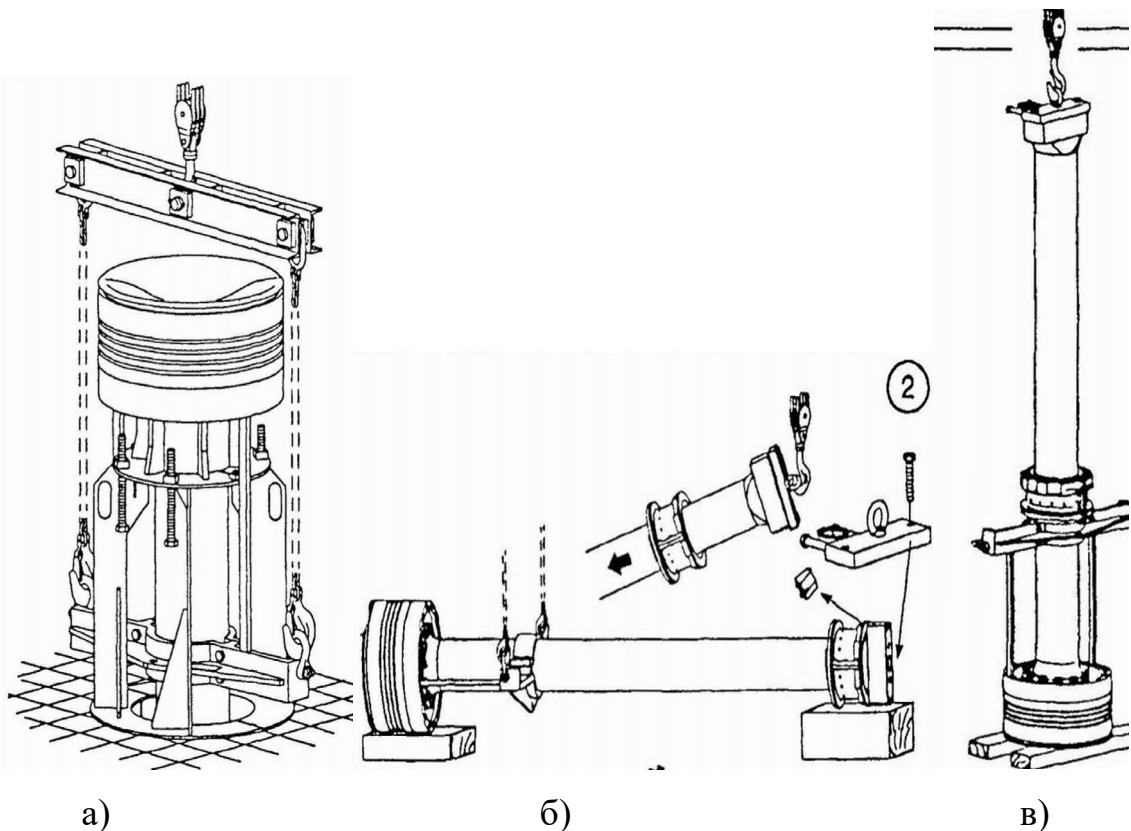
Підготовка поршня до випробування під тиском
